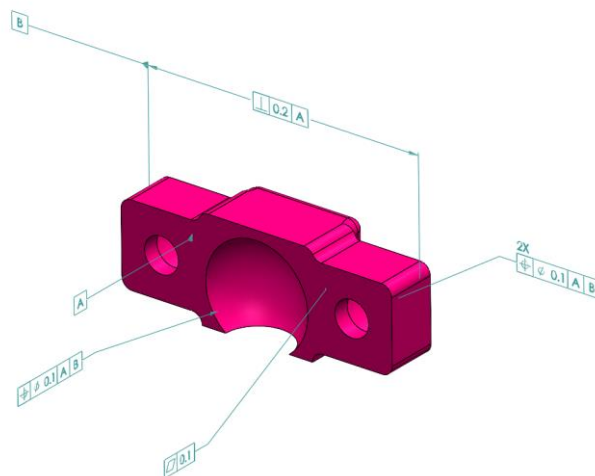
Tolerancias geométricas “Barra 2_2” pulgar
